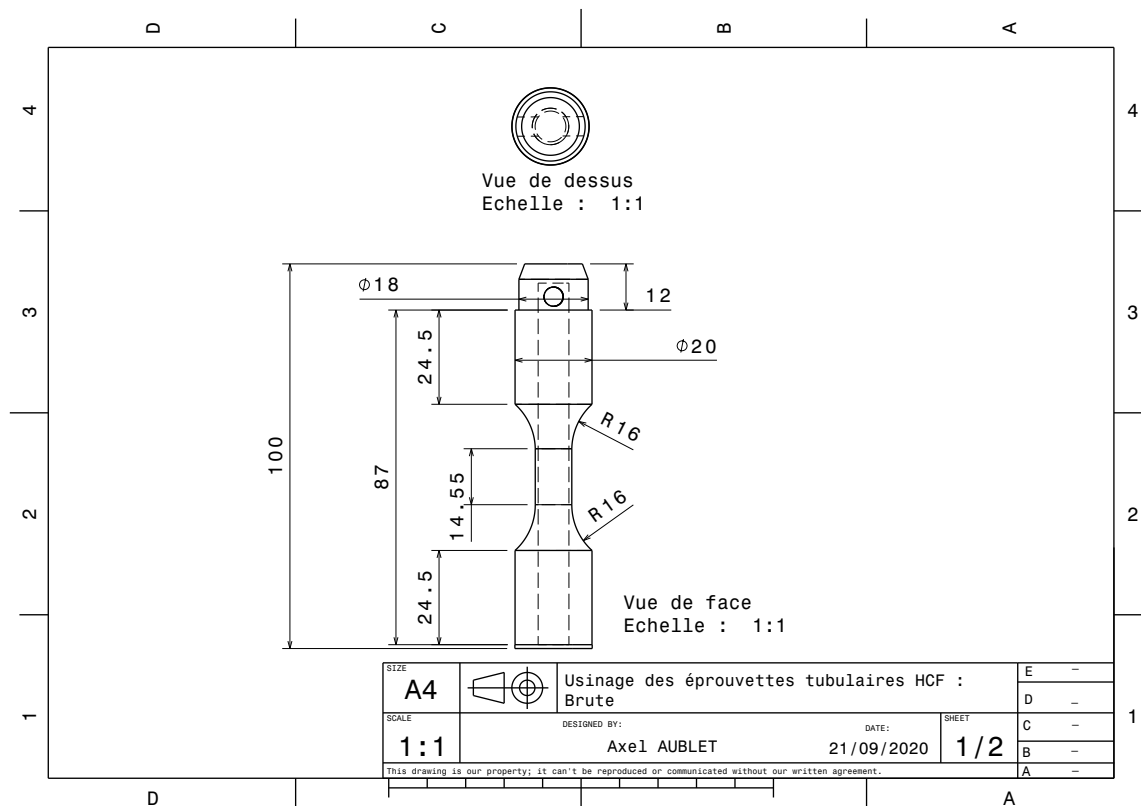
Dimensions nominales des éprouvettes brutes de fonderie.
